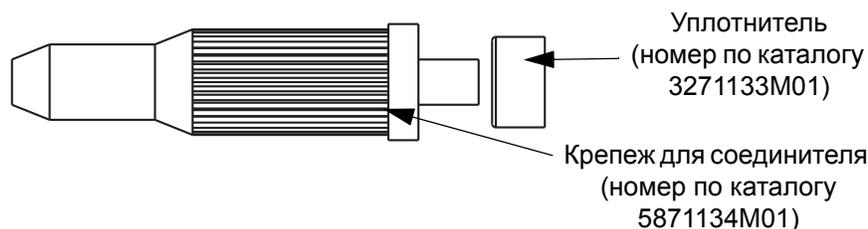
Крепеж для соединителя — соединительный уплотнитель для насоса
